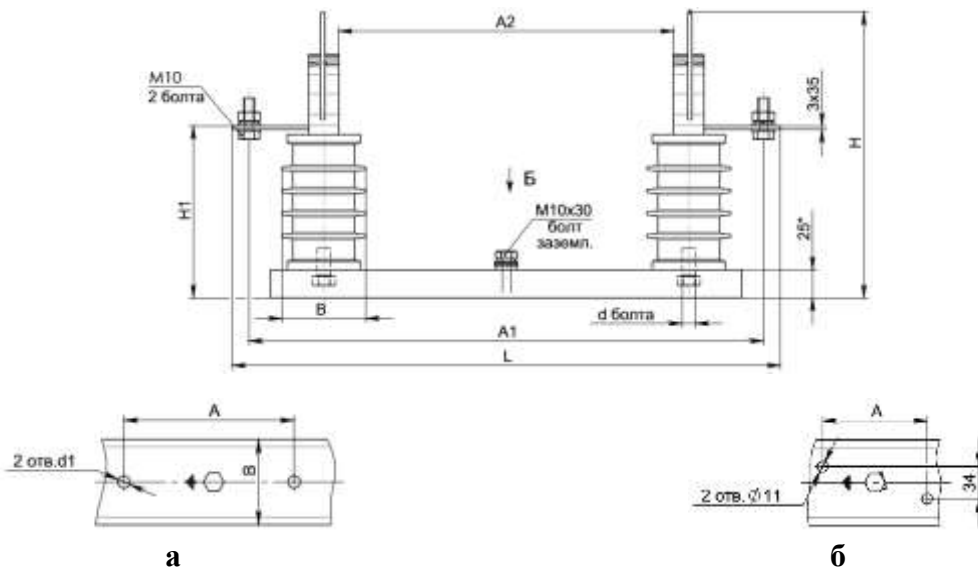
Габаритные, присоединительные и установочные размеры основания.
